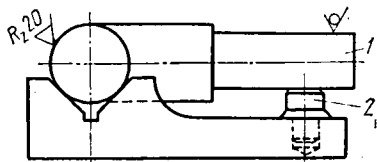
Установка заготовки детали с пересекающимися осями цилиндрических поверхностей
